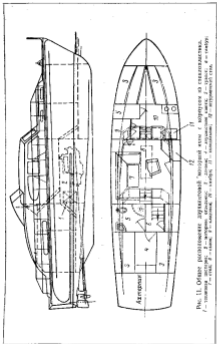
Общее устройство ливингетовой моторной яхты с корпусом из сталепластика.
